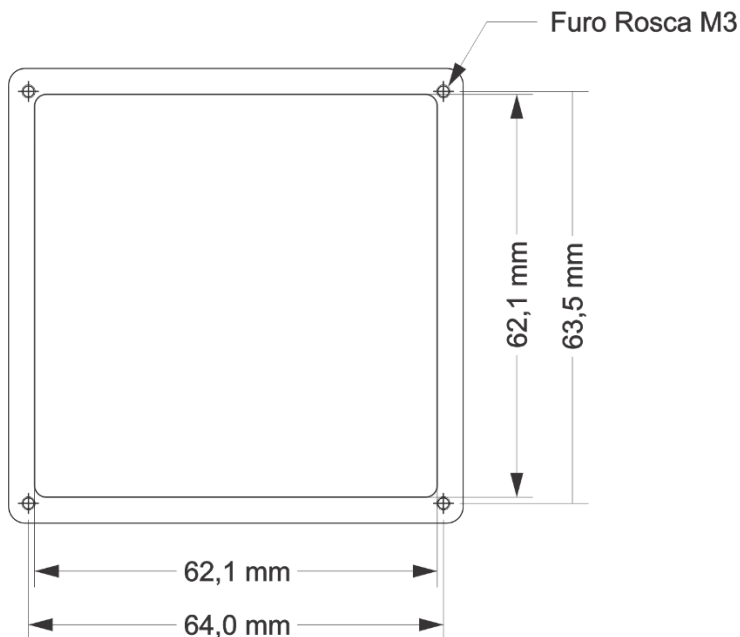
Dimensões do corte no painel para fixação do módulo PLNS.
